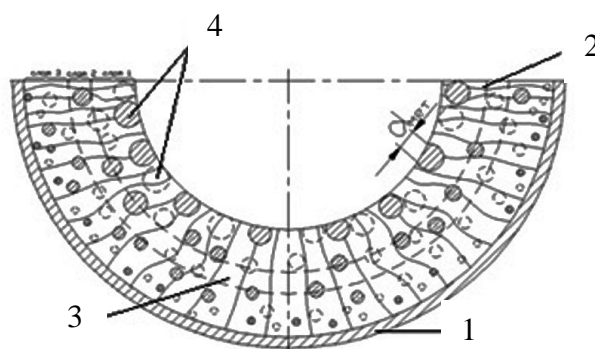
Вкладыш из модифицированной древесины и металлического наполнителя: 1 – втулка; 2 – вкладыш; 3 – матрица; 4 – теплоотводящий металлический наполнитель
